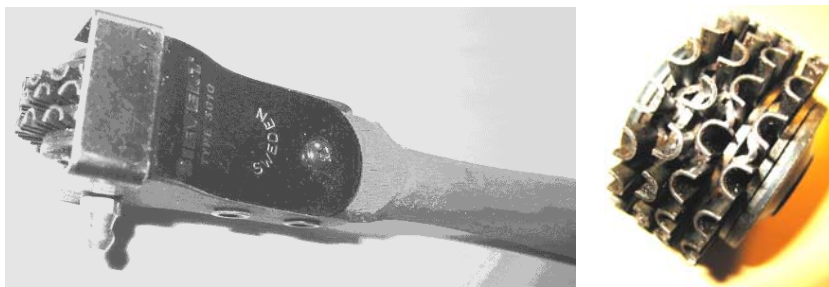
Ручная оправка и звездочка для профилирования круга обкатыванием
